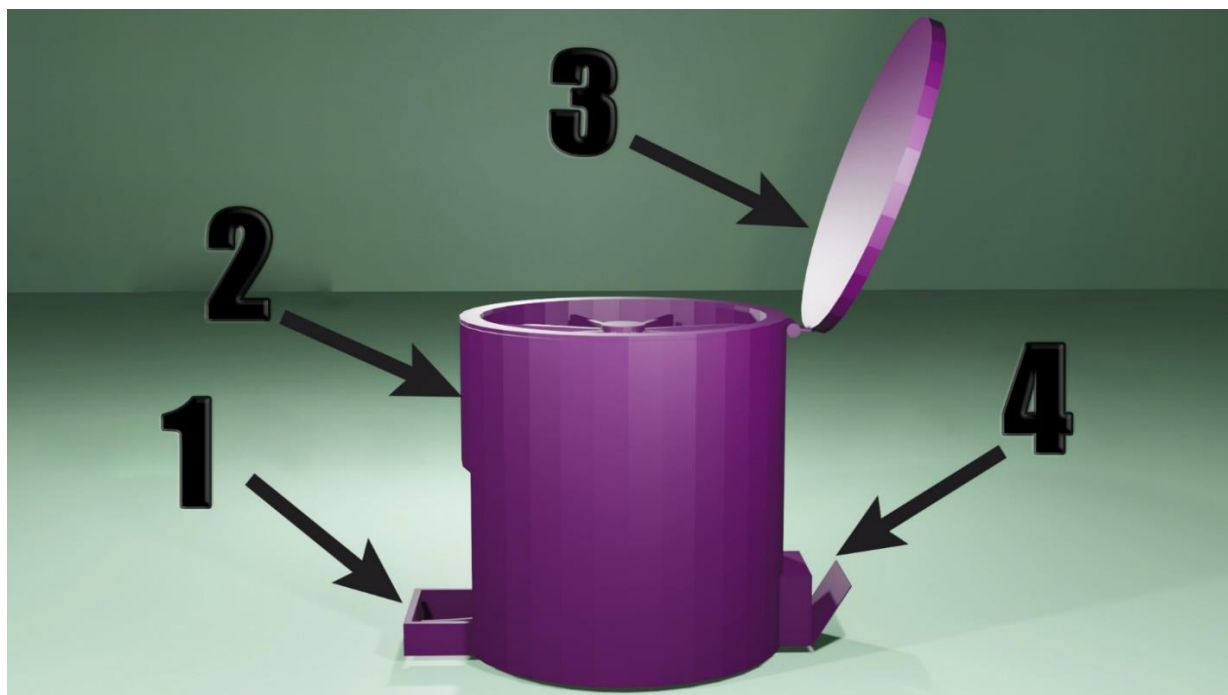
3D-модель корпусу Автоматизованого дозатору ліків: 1 – місце для стаканчика; 2 – корпус; 3 – зовнішня кришка; 4 – відсік блоку живлення
